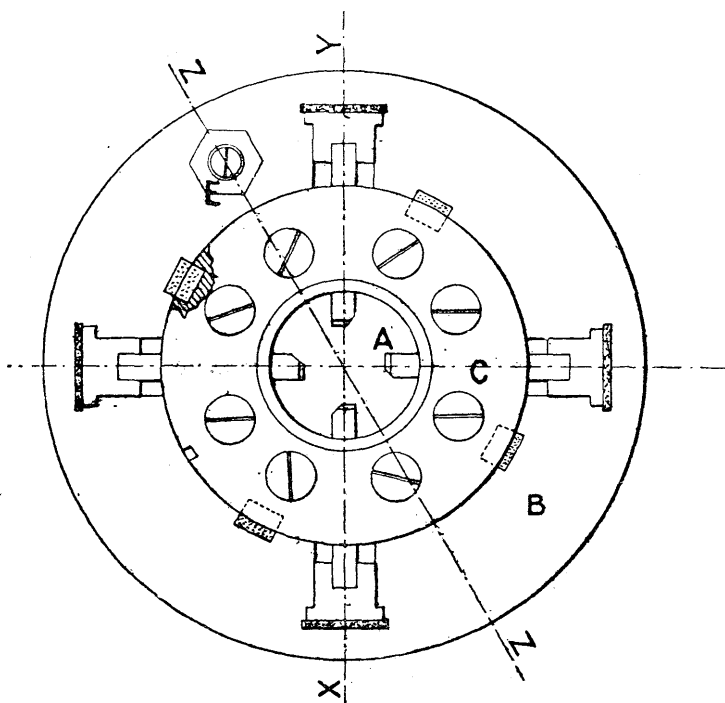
Disposition des filières de la taraudeuse Acme. — Vue par bout.
